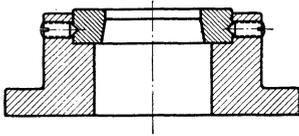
Befestigung der Schnittplatte durch Druckschrauben.
